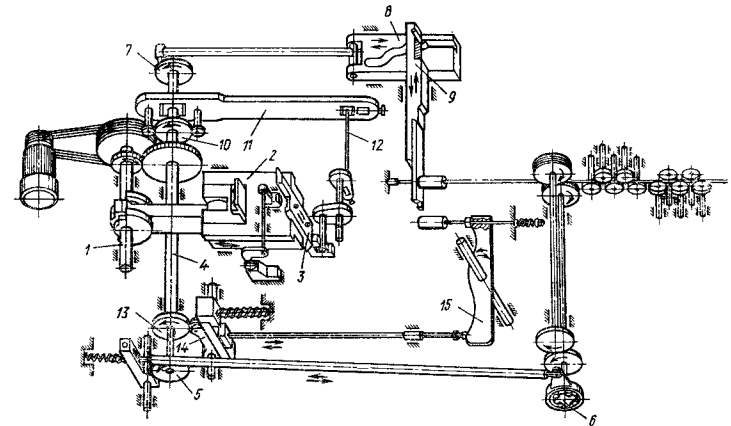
Схема холодновысадочного автомата для штамповки полупустотелых заклепок: 1 — коленчатый вал; 2 — высадочный ползун; 3 — пуансонные салазки; 4 — распределительный вал; 5 — кулак привода обгонной муфты; 6 — обгонная муфта для односкоростного привода подающих роликов; 7 — кривошипная шайба привода механизма отрезки; 8 — ползун механизма отрезки; 9 — ножовый шток; 10 — кулак для вертикального перемещения пуансонных салазок; 11 — кулиса привода пуансонных салазок; 12 — качающийся вал; 13 — кулак привода выталкивателя; 14 — кулиса; 15 — рычаг выталкивающего механизма
